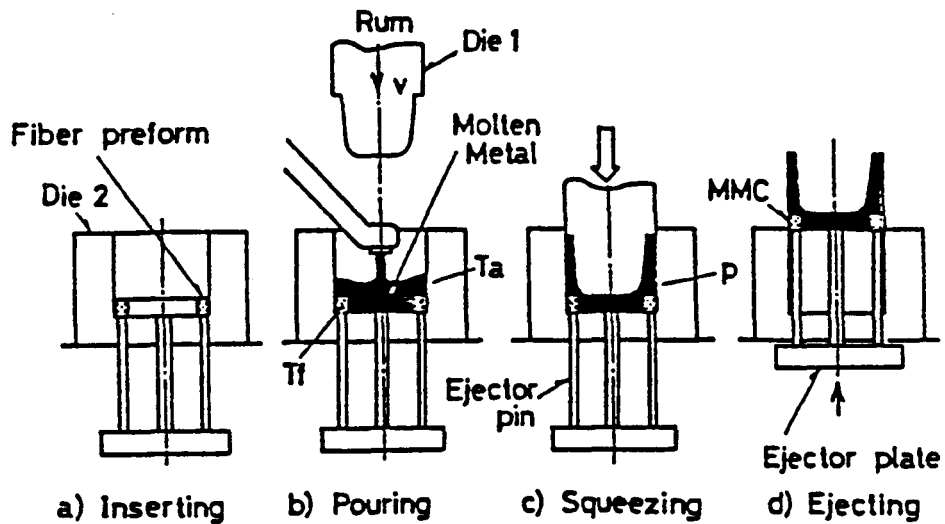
Différentes opérations du procédé de Squeeze Casting durant lesquelles le métal liquide est coulé de manière directe dans la préforme. [26]
